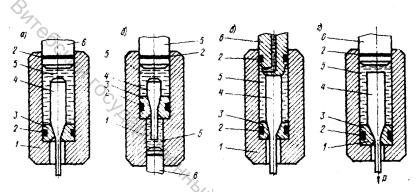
Основные способы гидропрессования жидкостью: а – простое гидропрессование; 6 – гидропрессование с противодавлением; в – гидромеханическое прессование; r – гидропрессование с передним натяжением.
